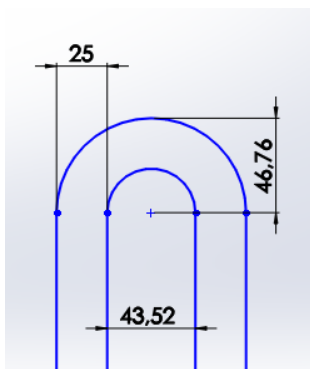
Cotas de los codos del serpentín del disipador de calor. Fuente: propia. Realizado en SolidWorks.
